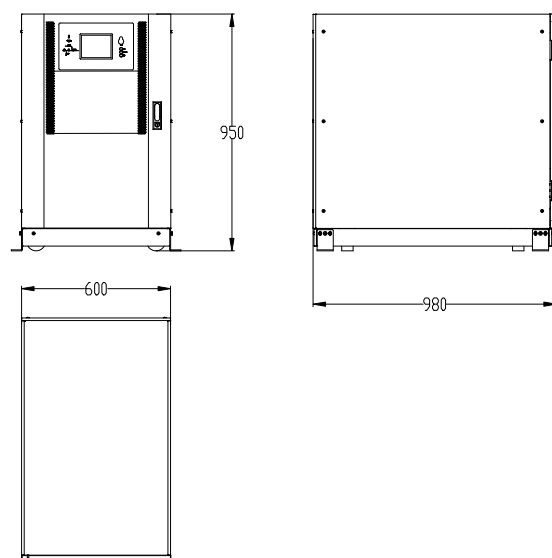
Taille de l'UPS 60KVA (unité: mm)
